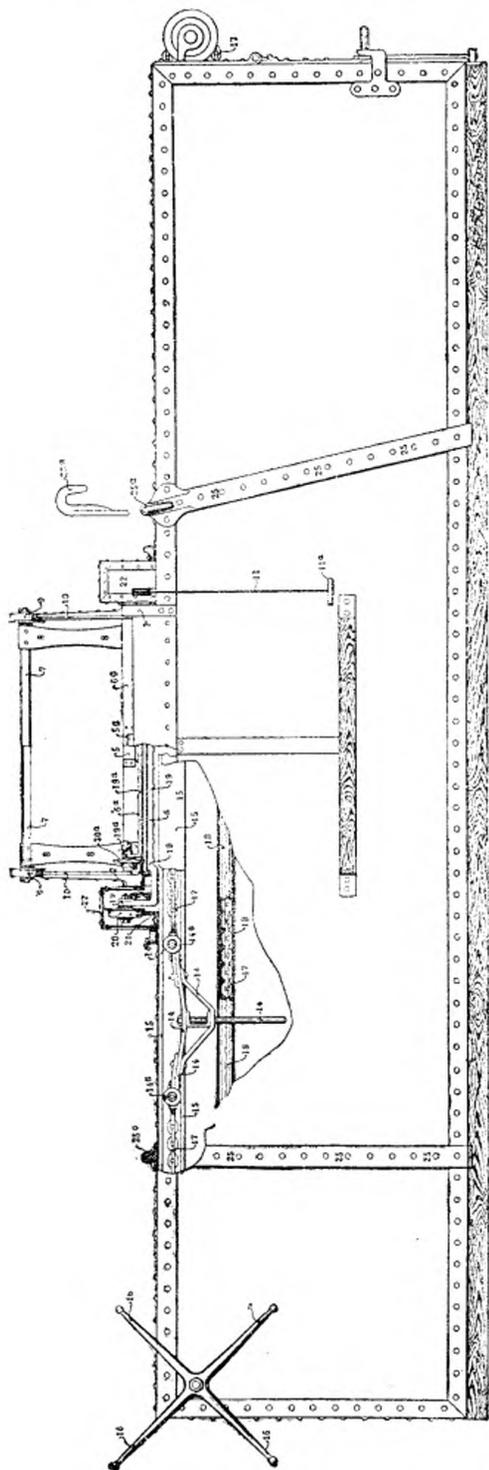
Vue et coupe longitudinale du caisson de la voiture Kinsbruner.
